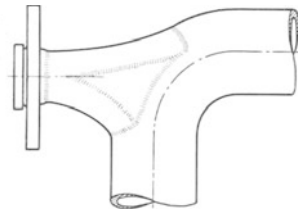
Schweißung von Bogenabzweigungen.
